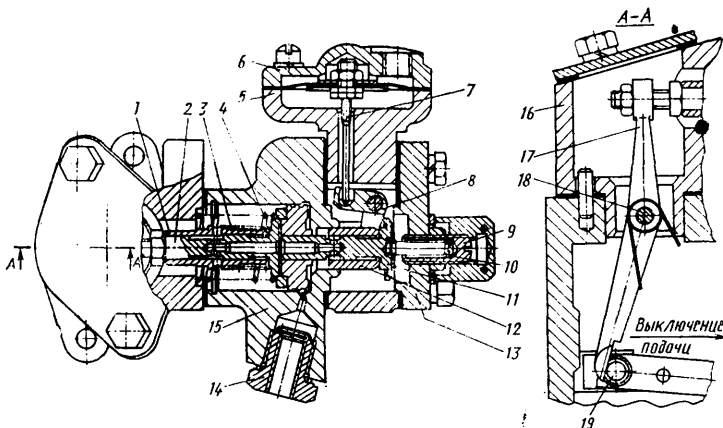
Корректор подачи топлива по наддуву: 1 — гильза упора; 2 — упор; 3 — пружина гильзы упора; 4 — пружина поршня; 5 — корпус мембраны; 6 — крышка мембраны; 7 — мембрана со штоком; 8 — рычаг корректора; 9 — корпус пружины корректора; 10 — пружина корректора; 11 — золотник корректора; 12 — поршень корректора; 13 — крышка корректора; 14 — ввертыш; 15 — корпус корректора; 16 — проставка корректора; 17 — рычаг; 18 — ось рычага; 19 — ось рейки
